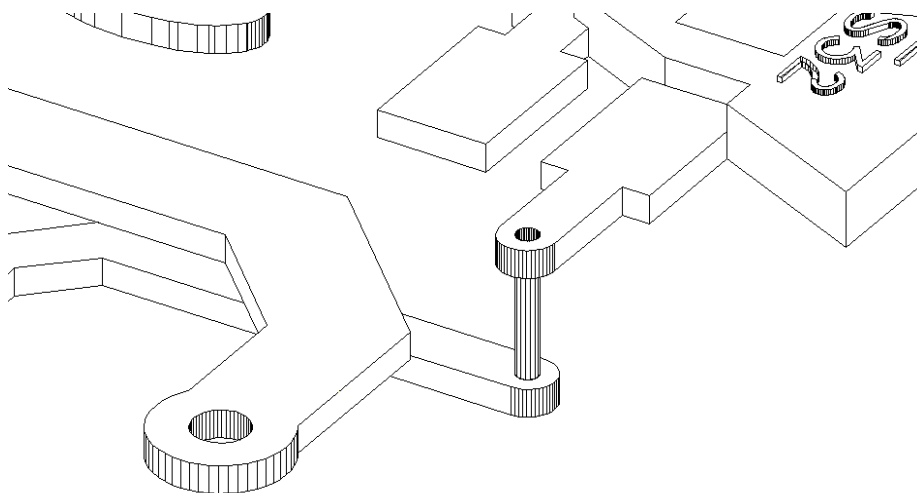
Estructura de una vía. Se ha omitido la base de baquelita para mostrar las pistas de la cara de soldadura (la cara de abajo).
